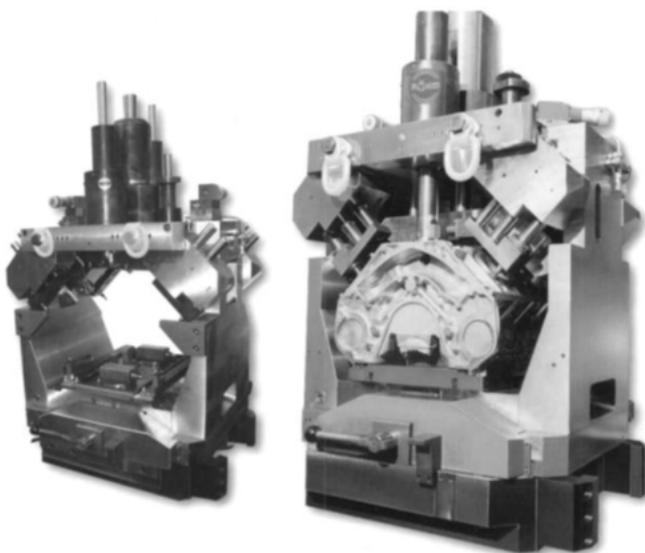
Приспособление с гидравлическим приводом для установки блоков двигателей
